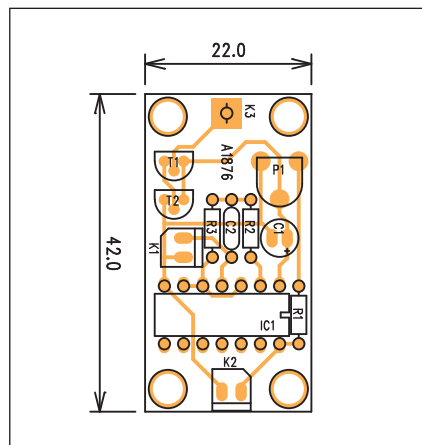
Obrazec desky spojů testeru (strana BOTTOM)
